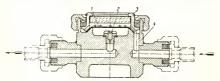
Фильтр с дросселем I — фильтрующая ткань; 2 — дроссель; 3 — крышка; 4 — корпус фильтра
